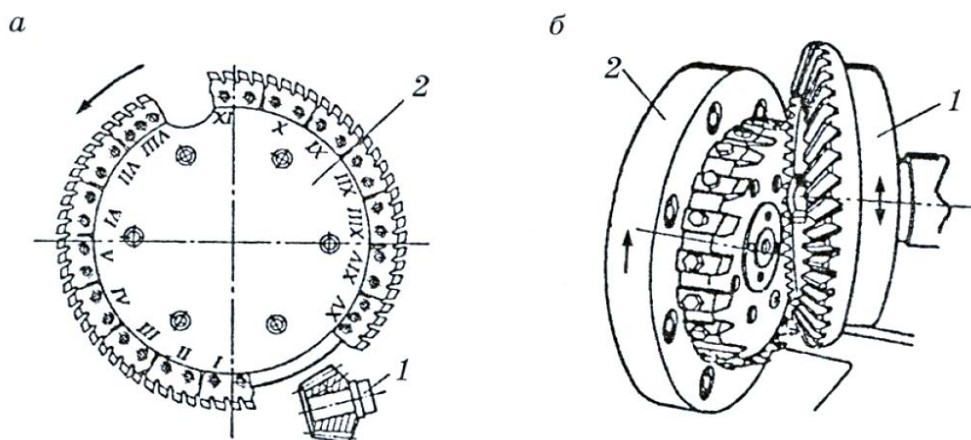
Нарезание зубьев конических колес: а – протягивание круговой протяжкой; б – резцовой головкой-протяжкой; 1 – обрабатываемое зубчатое колесо; 2 – инструмент
